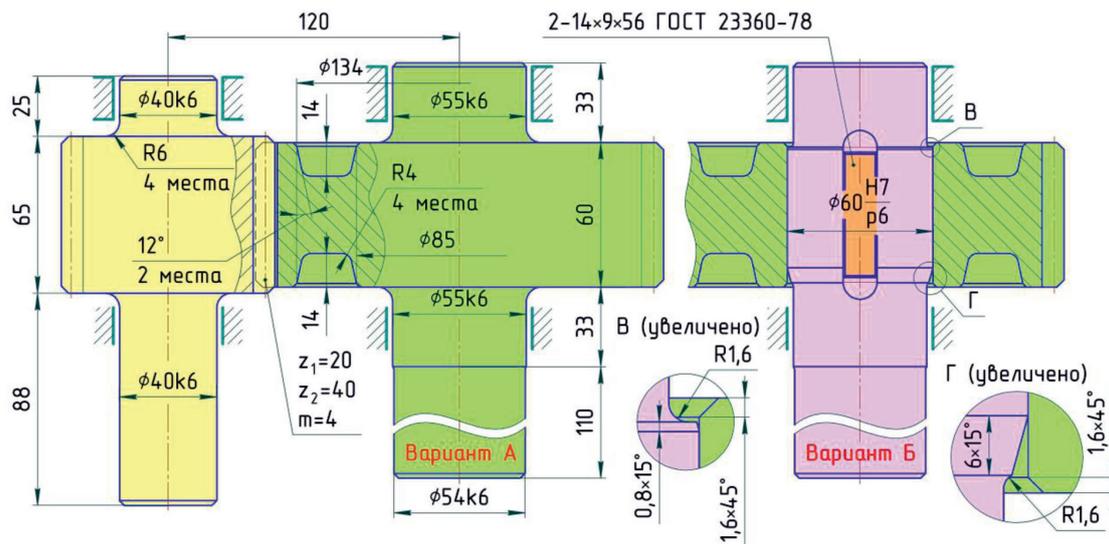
Рассчитываемая зубчатая передача с двумя вариантами (А, Б) исполнения тихоходного узла передачи
